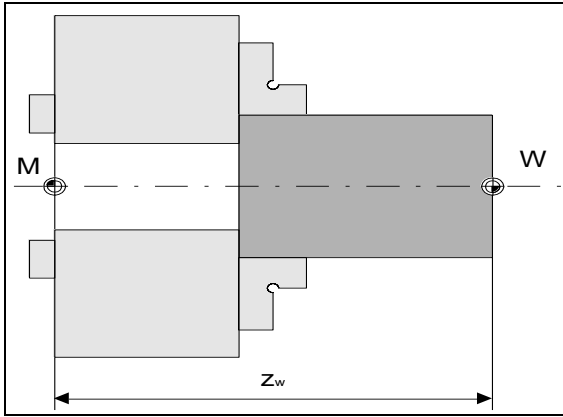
Установка нулевой точки заготовки на токарном верстаті з ЧПК
